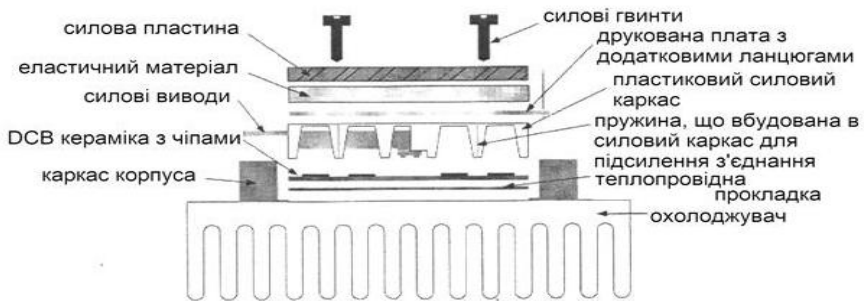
Конструкція модуля SKiiPPACK
